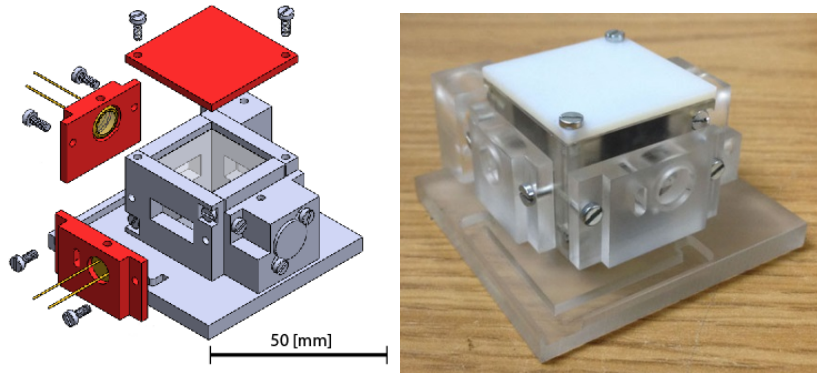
17 Ensamble del prototipo de sistema mecánico
